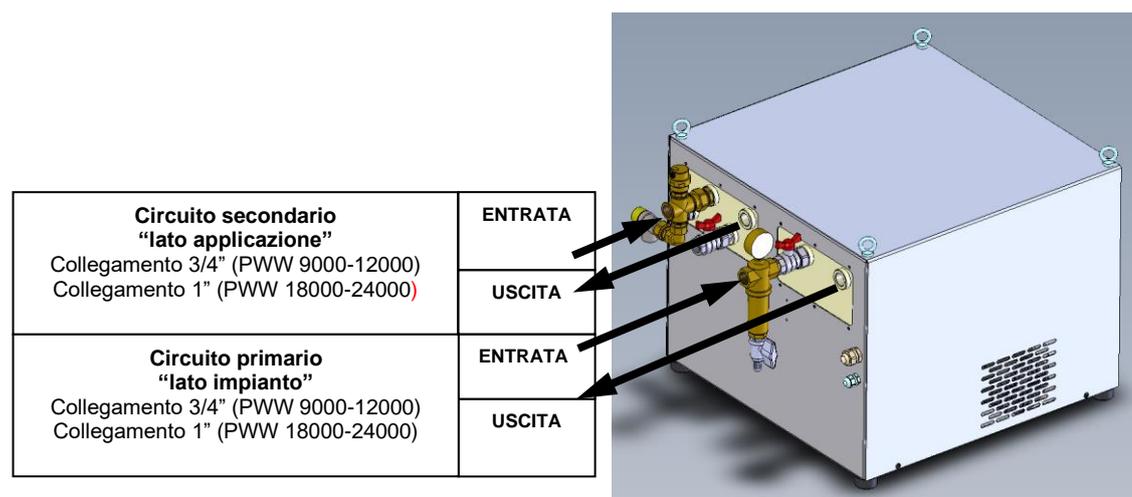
b – Piastre per i collegamenti idraulici (PWW)
